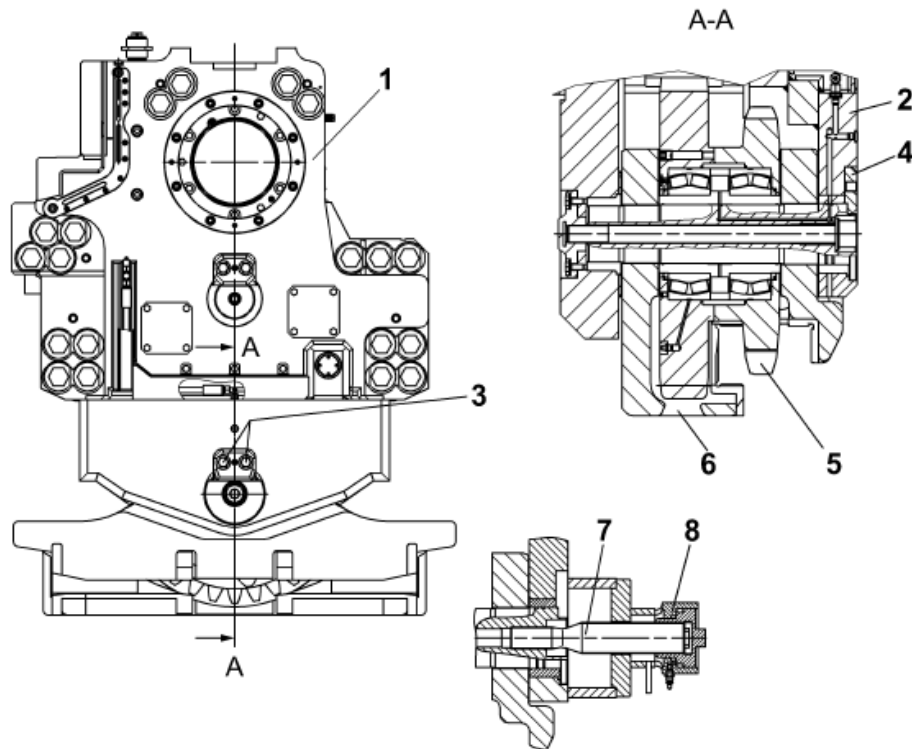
Бесцепной цевочно-реечный механизм подачи
